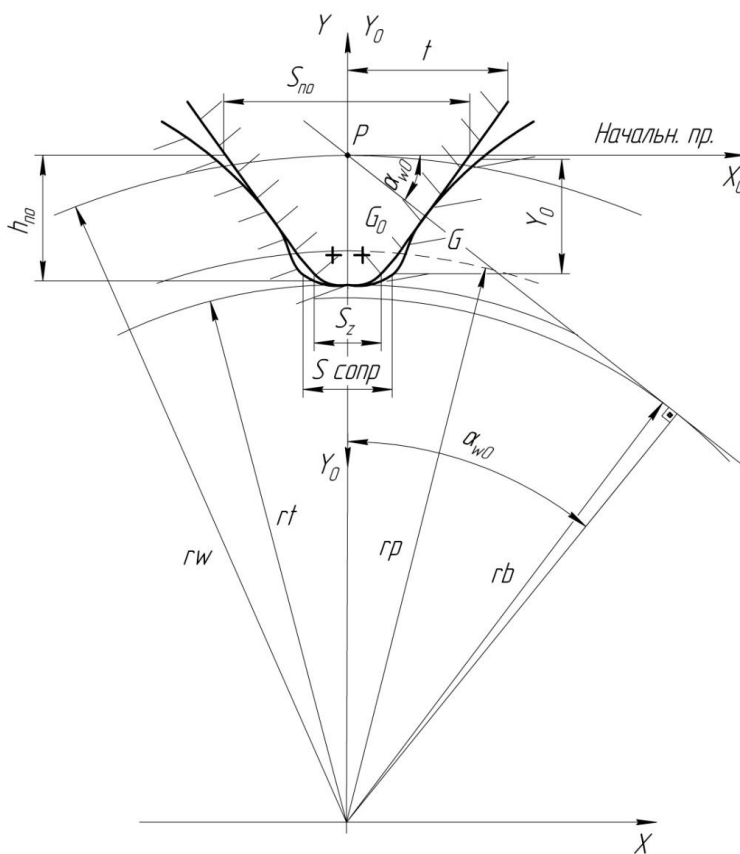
Схема формирования эвольвентного зуба фрезы
